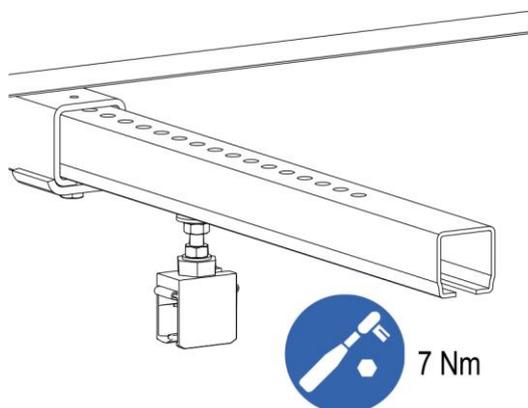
Premier support de rail glissé dans le bras de serrage et serré
